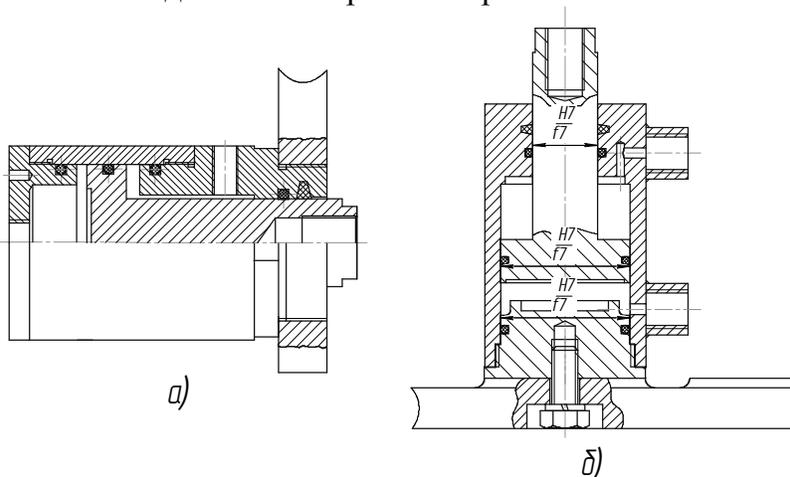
Крепление гидроцилиндров (а – по наружной резьбе; б – по внутренней резьбе)
